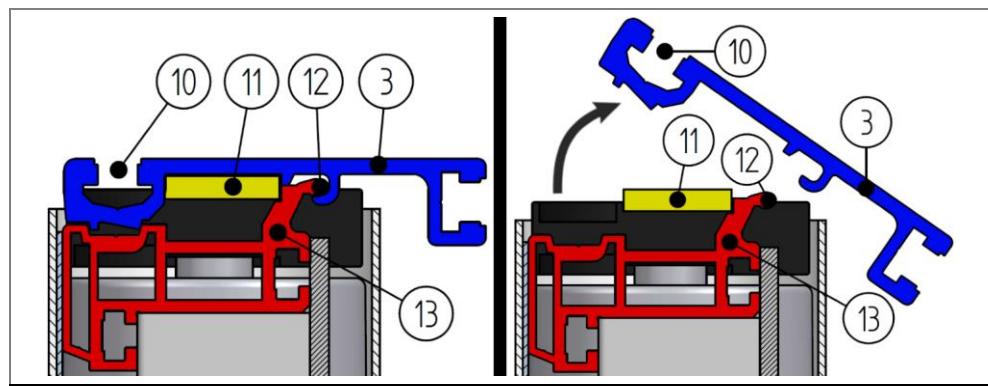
Explosivní výkres: Těleso dopravního pásu
